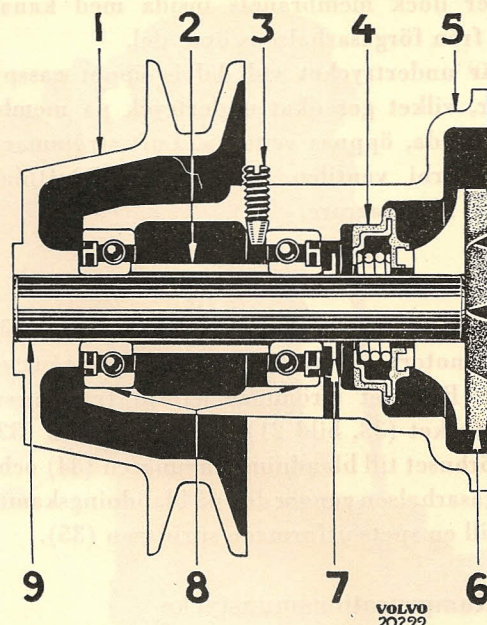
Vattenpump sen. utf. Monterad fr. o. m. motornr 8669.
